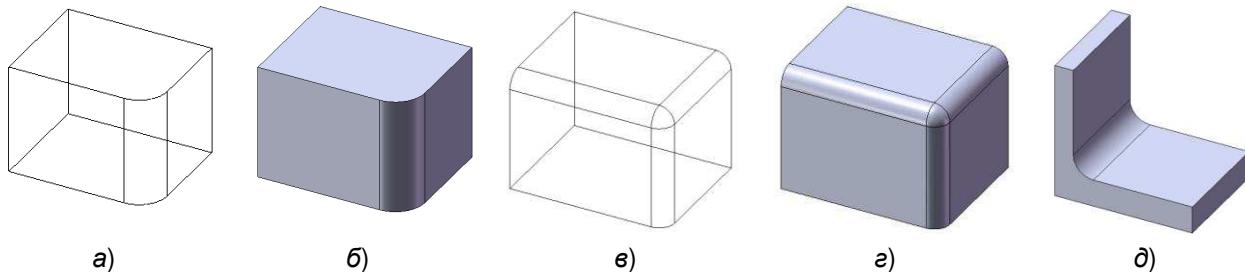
Функции скругления: а, б – скругление ребер; в, г – скругление вершин; д – скругление с добавлением материала (выкружка – filleting)
